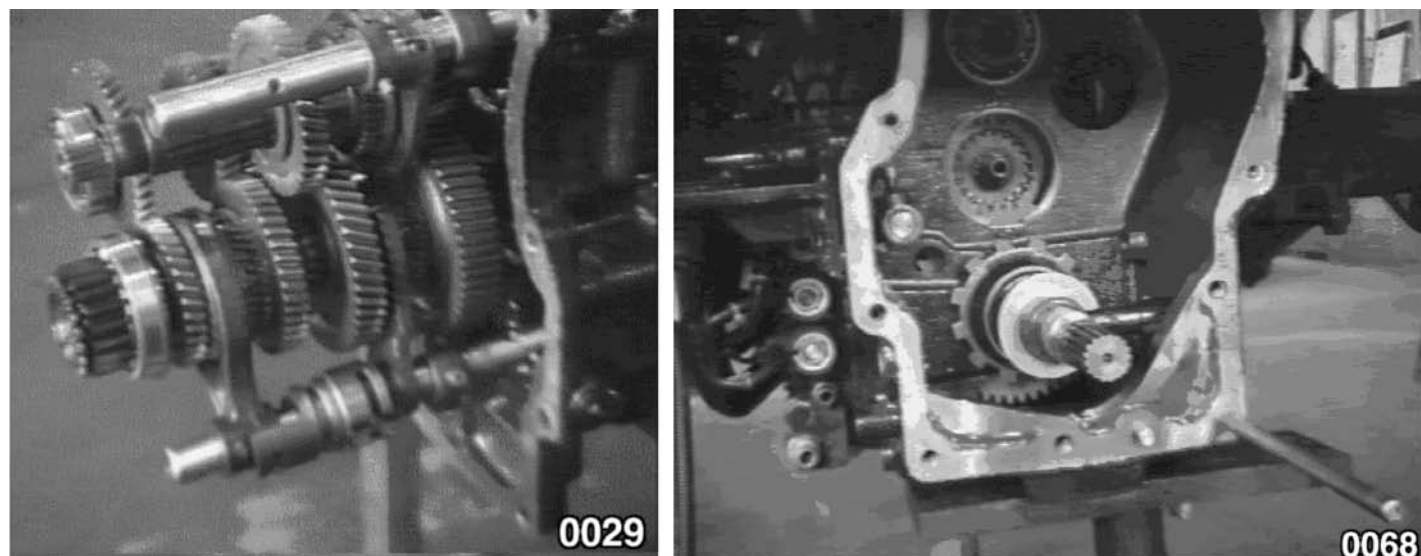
Désaccouplement du carter de boîte avant de la boîte arrière.
